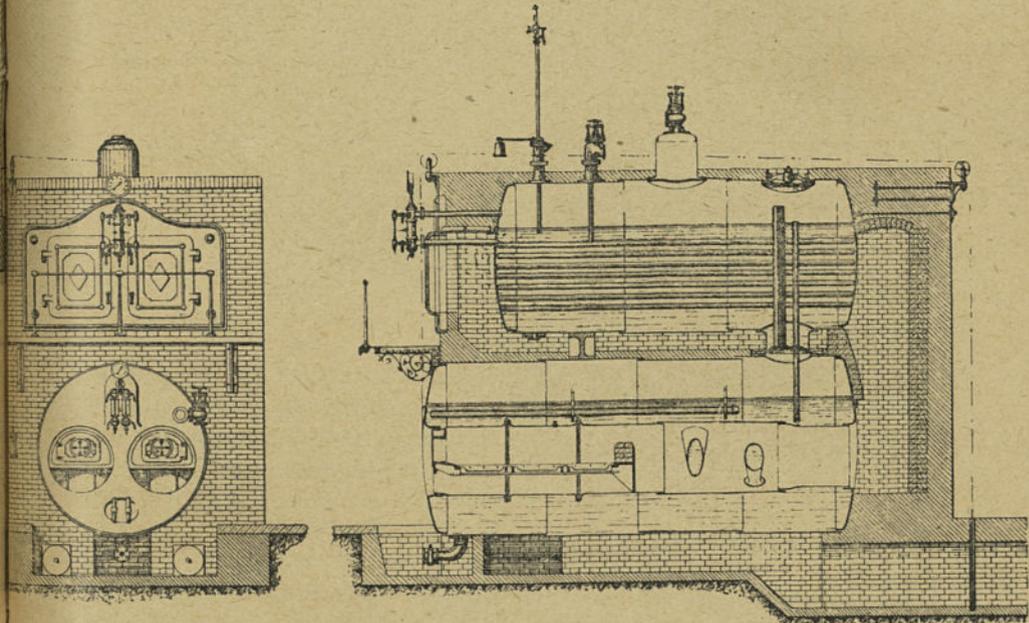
Générateur Tischbein à 2 plans d'eau et à tubes Galloway (construction Piedbœuf).
